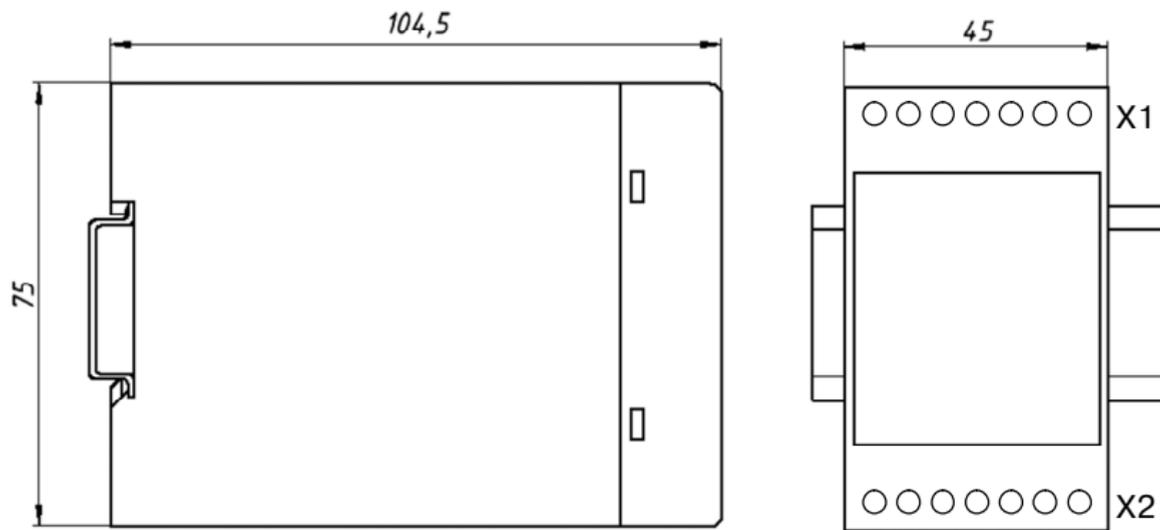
Габаритные и присоединительные размеры преобразователя
